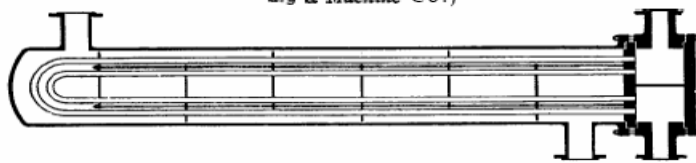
Intercambiador 1-2 con tubos en U. (Patterson Foundry & Machine Co.)
